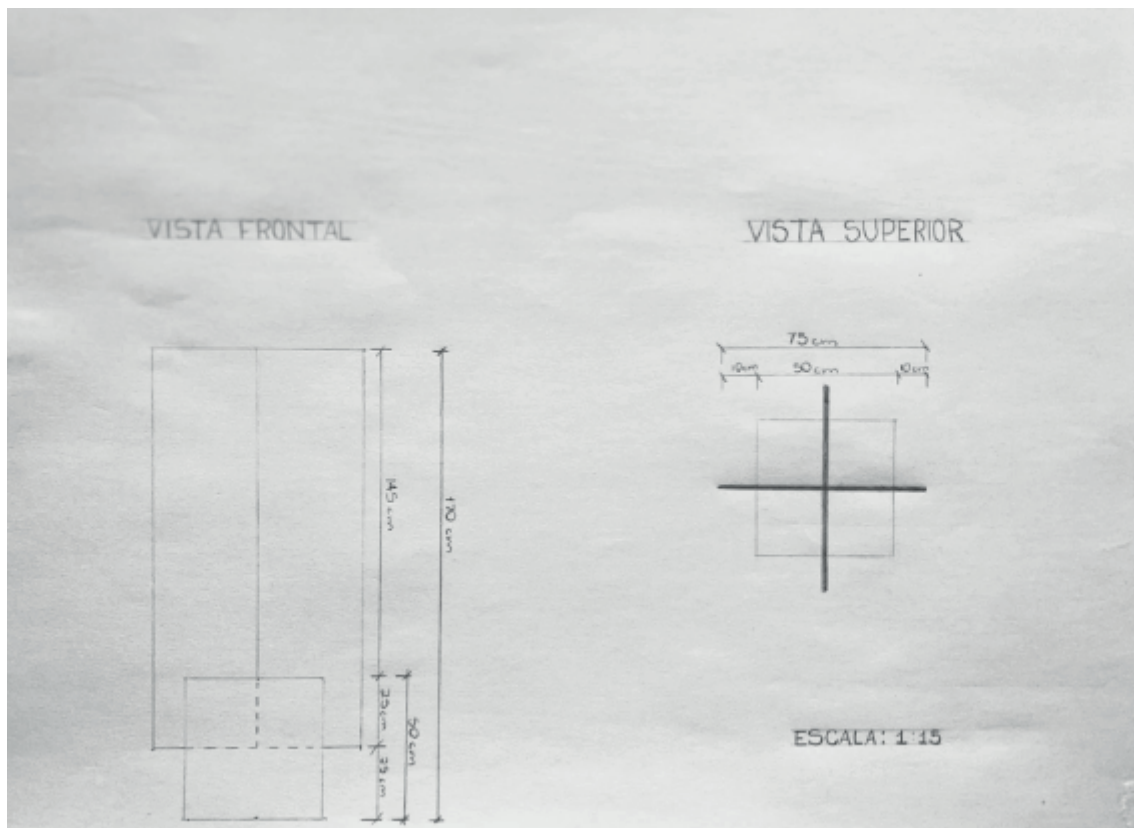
Desenho Técnico com vistas - Superior e Frontal
